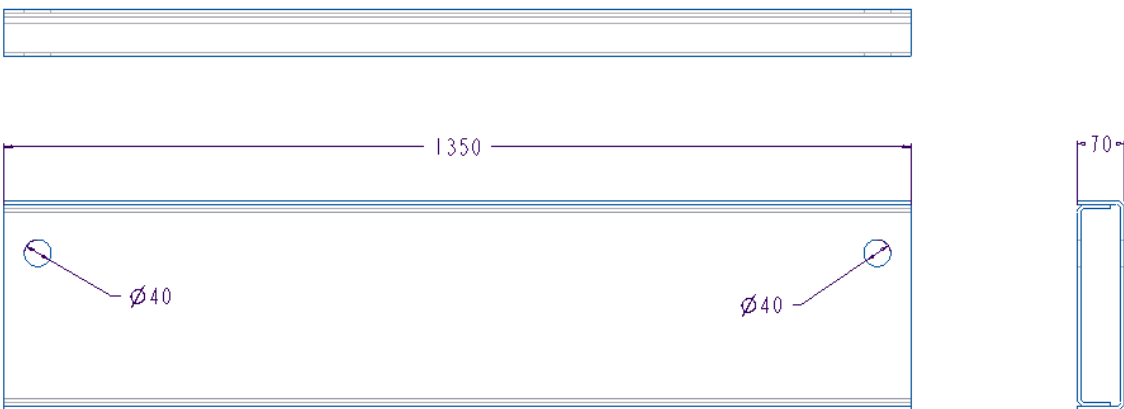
Dibujo dimensional de la pieza de trabajo. Vistas ortográficas. Cotas en mm.
